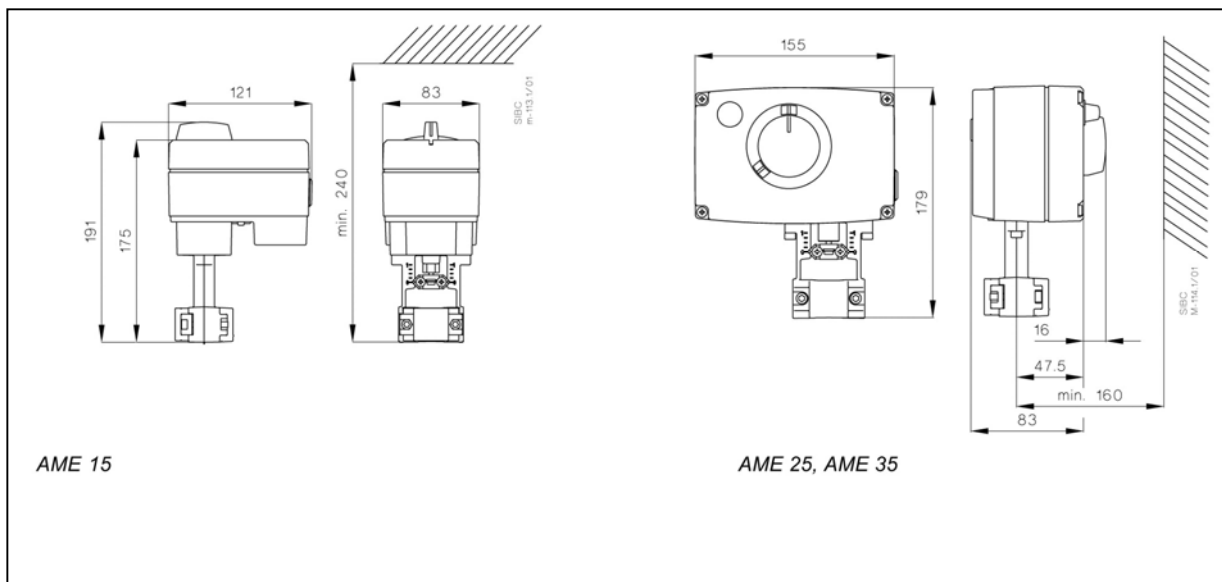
Габаритные и присоединительные размеры AME 15, 25, 35.
